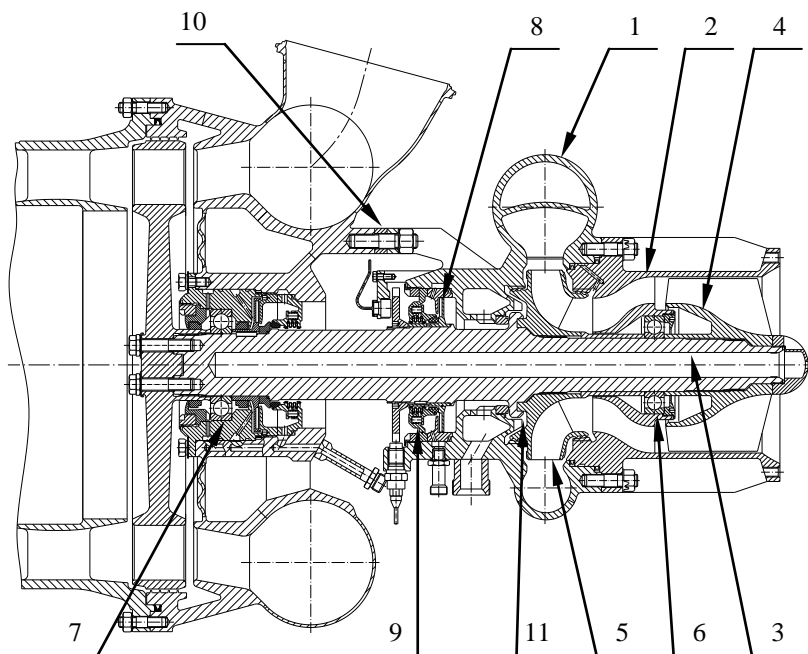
Насос окислителя с турбиной: 1 – корпус; 2 – входной патрубок; 3 – вал; 4 – шнек; 5 – крыльчатка; 6 и 7 – подшипники; 8 – импеллер; 9 – торцовое уплотнение; 10 – шпонка; 11 – полость автоматического разгрузочного устройства
